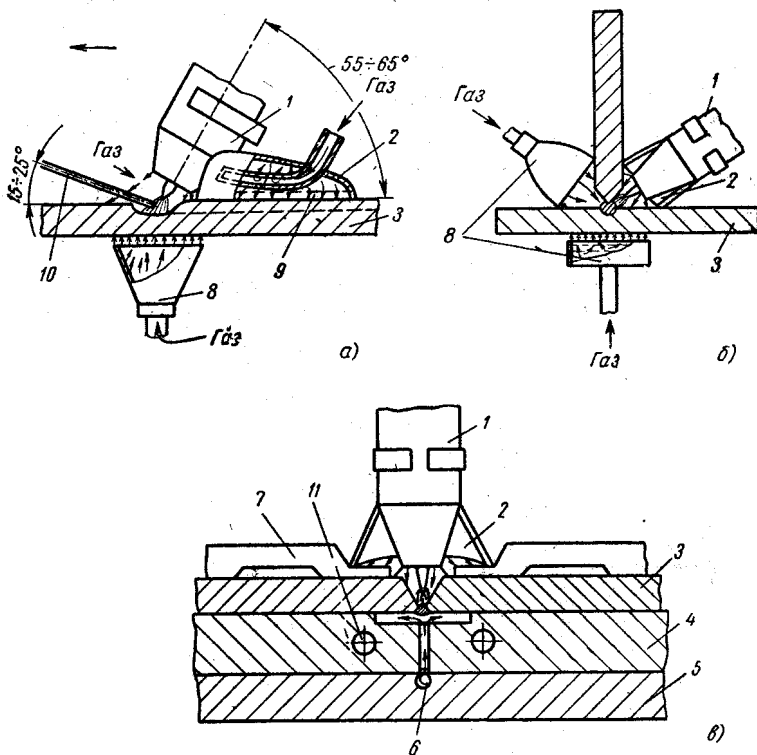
Схема защиты стыковых и тавровых соединений титана и его сплавов при аргоно-дуговой сварке: а, б – с применением поддува; в – с применением охлаждающих подкладок:
